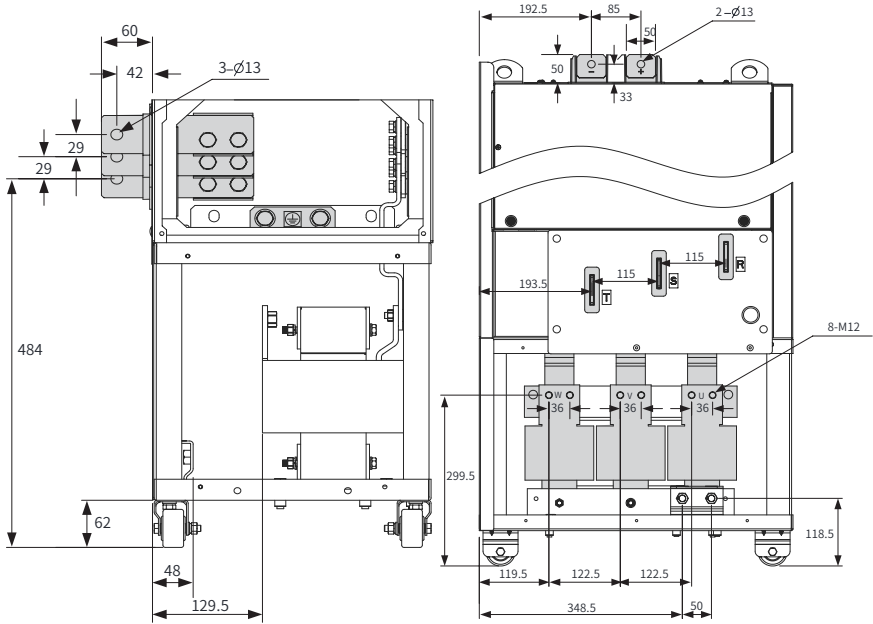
Размеры клемм главной цепи MD880-01S-0538-4(-L)/MD880-01S-0605-4(-L) (с выходными реакторами)
